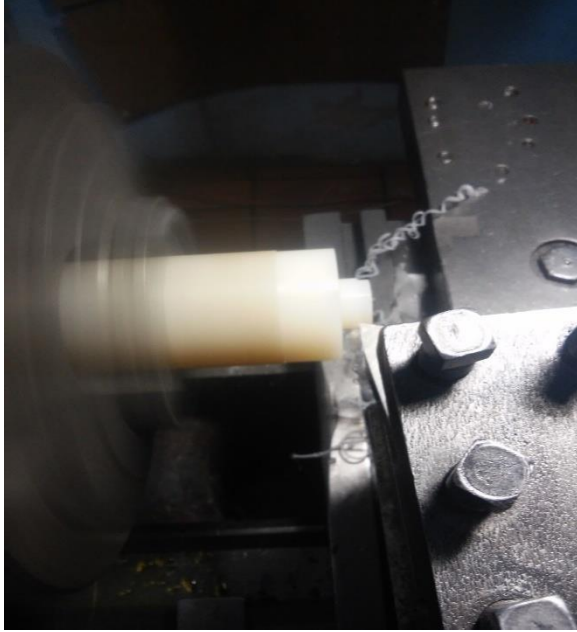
Maquinado en torno de cilindro para engrane 20 dientes.
